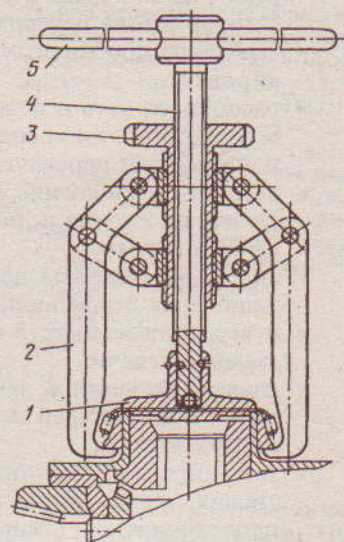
Съемник подшипника дифференциала: 1 - упор; 2 - лапка съемника; 3 - втулка с маховиком; 4 - винт; 5 - рукоятка съемника
